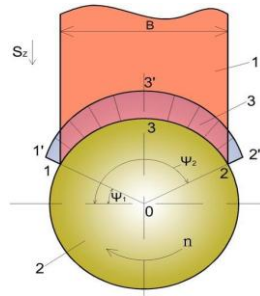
Схема фрезерования блока мяса цилиндрической фрезой 1 – блок мяса; 2 – фреза; 3 – эпюра толщины срезаемого слоя. B – ширина блока мяса; n – частота вращения фрезы; S_z – подача на зуб; Ψ_1, Ψ_2 – углы входа и выхода фрезы.
